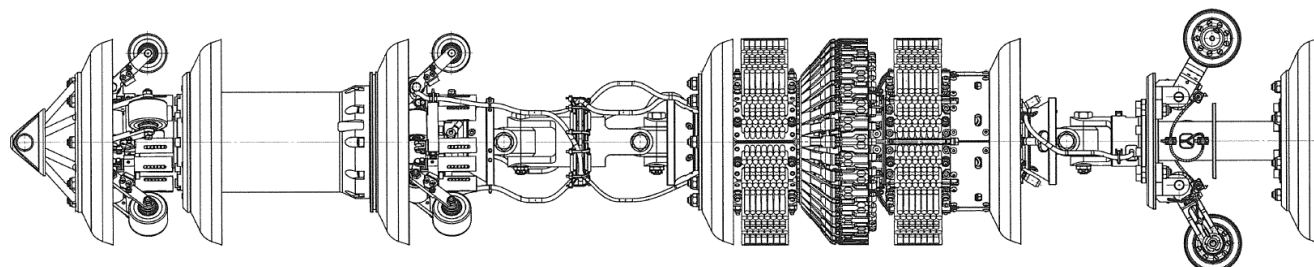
Чертеж общего вида дефектоскопа внутритрубного магнитного 12-MCK.01-00.000-01 и 14-MCK.01-00.000-01
